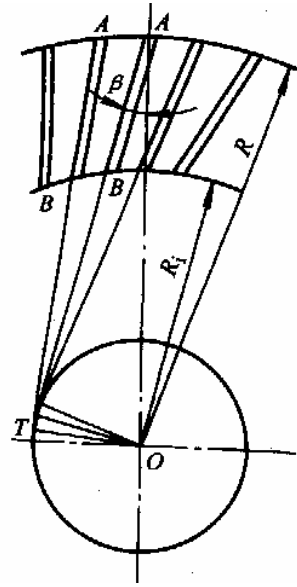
43 斜齿圆锥齿轮螺旋角 β 的测量
